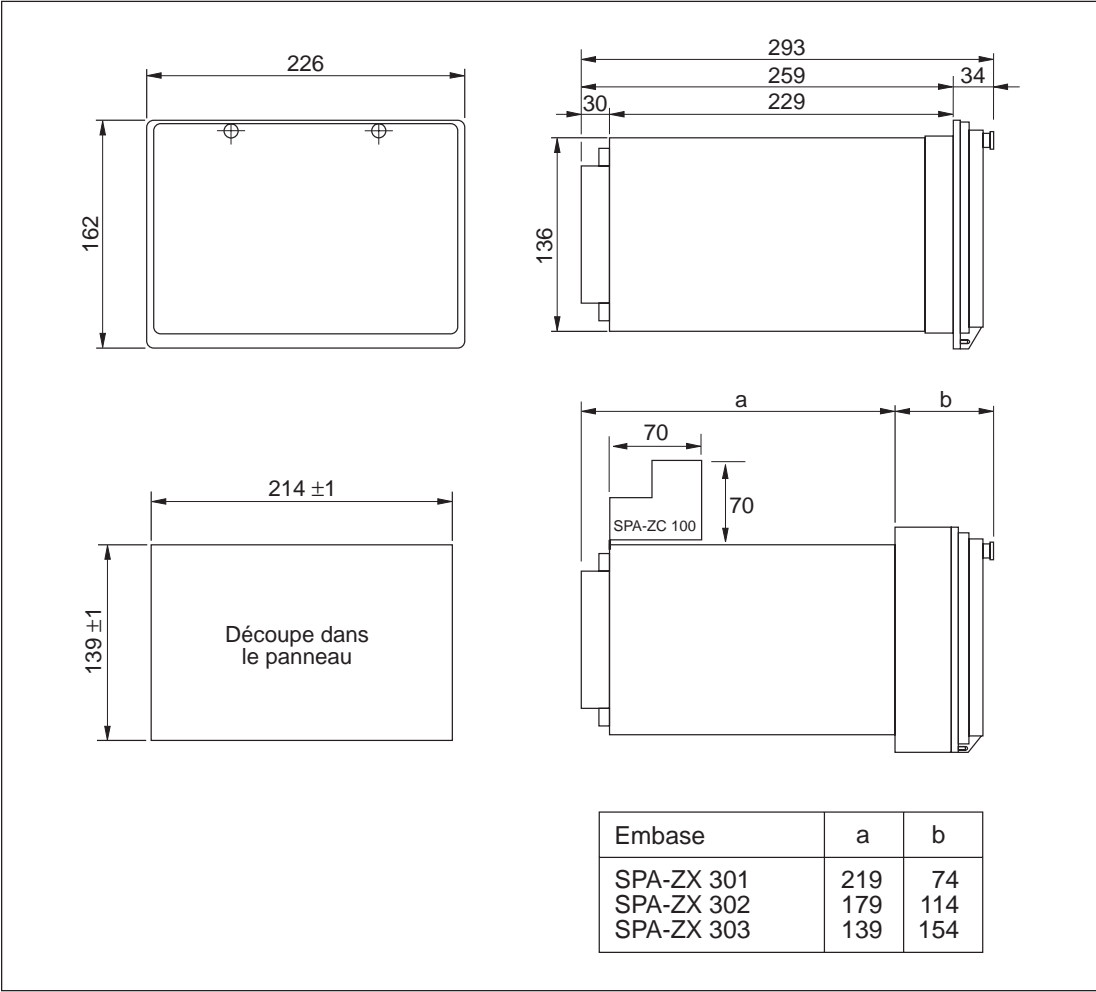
Schémas d'encombrement et de montage du régulateur de tension SPAU 341 C.
